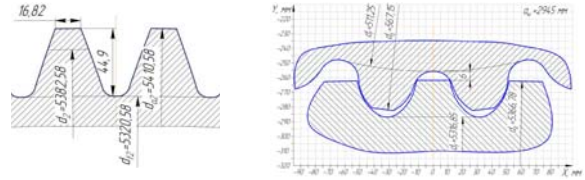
Эвольвентный профиль колеса и профили зацепления Новикова
